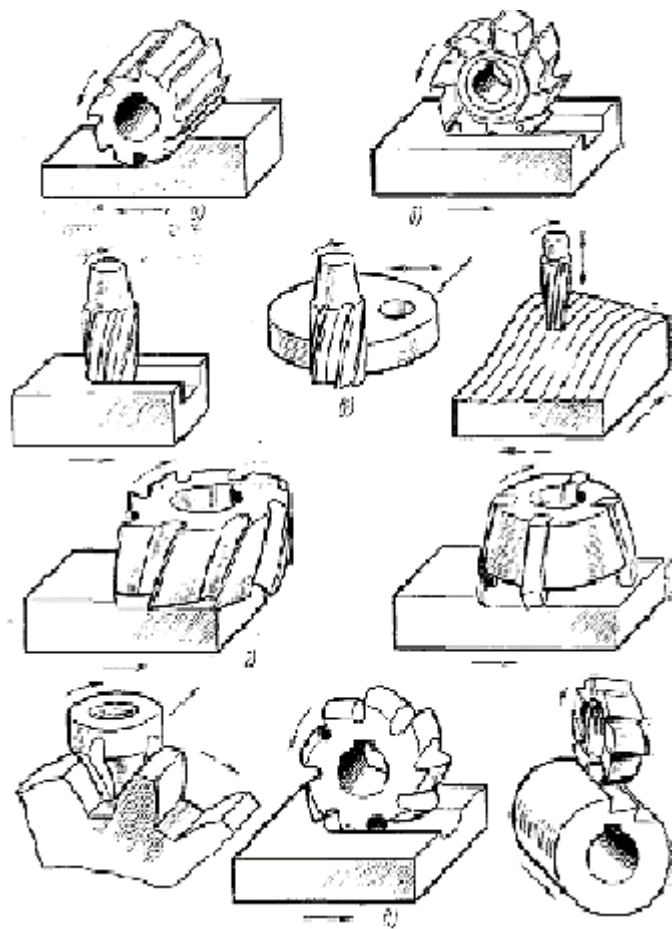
Основні типи фрез та оброблюваних ними поверхонь
